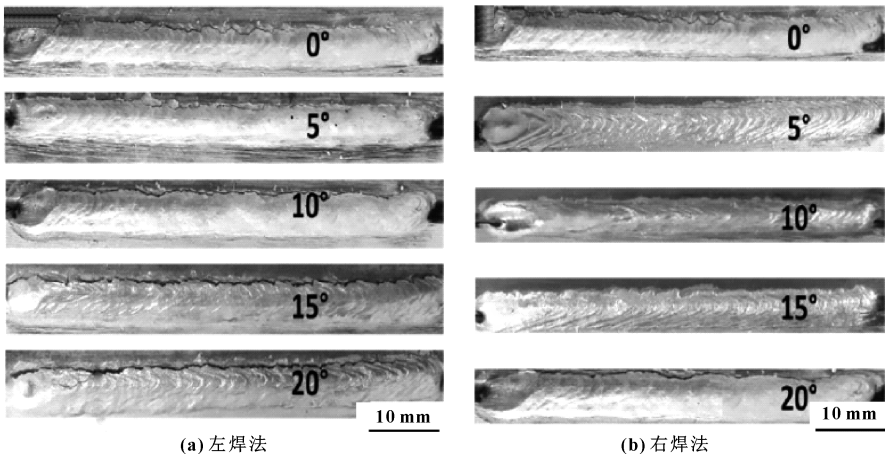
焊接方向 & 焊枪角度对焊缝表面形貌的影响
